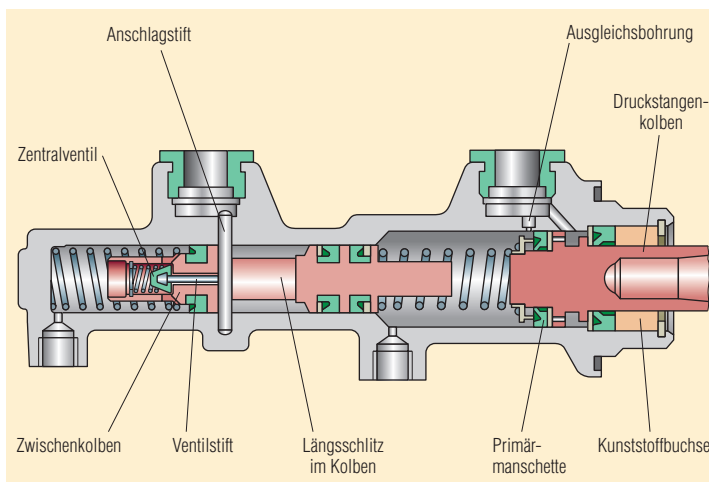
Gestufter Tandem-Hauptzylinder mit Zentralventil.
